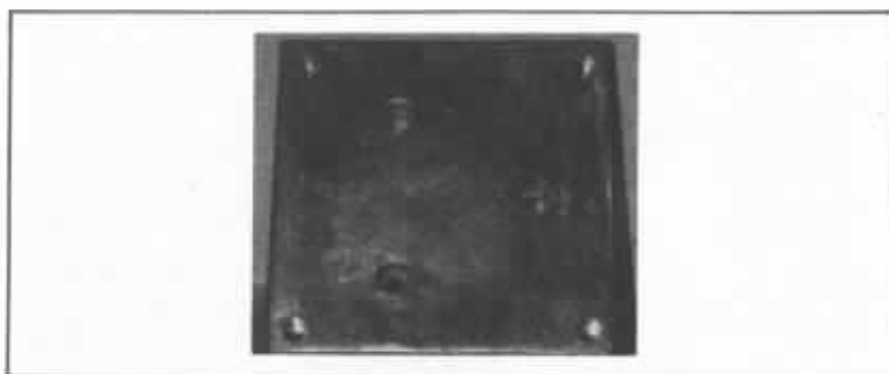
Le support du moteur terminé, après coulage et usinage des trous de fixation.
